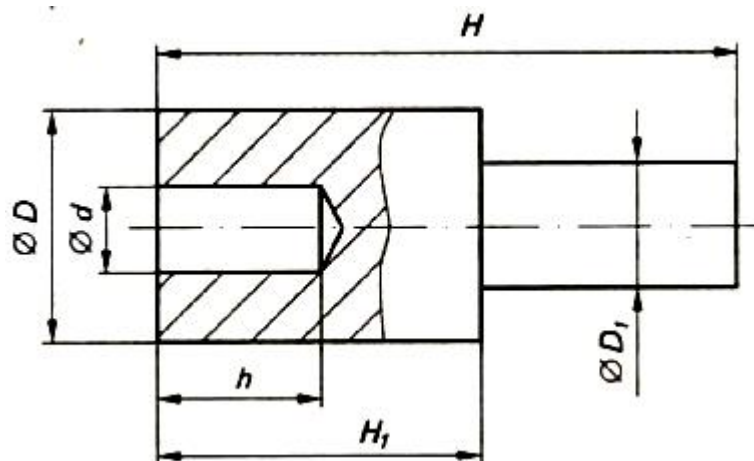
Эскиз детали «Ступенчатый валик»
